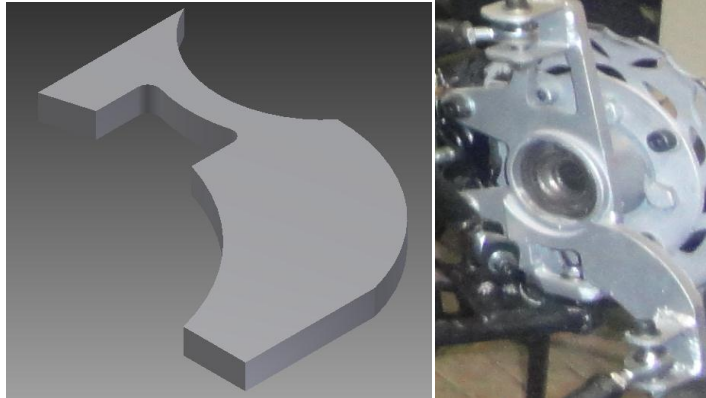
Brazo de acoplamiento ensamblado en mangueta
